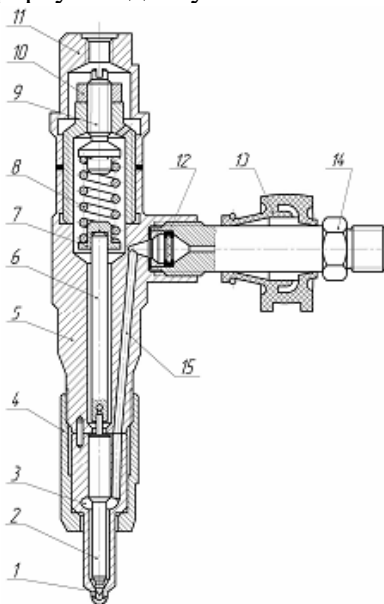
Форсунка: 1 – соплові отвори; 2 – голка; 3 – корпус розпилювача; 4 – гайка розпилювача; 5 – корпус; 6 – шток; 7 – опорна шайба; 8 – пружина; 9 – регулювальний гвинт; 10 – контргайка; 11 – ковпак; 12 – сітчастий фільтр; 13 – ущільнювач; 14 – штуцер; 15 – канал
